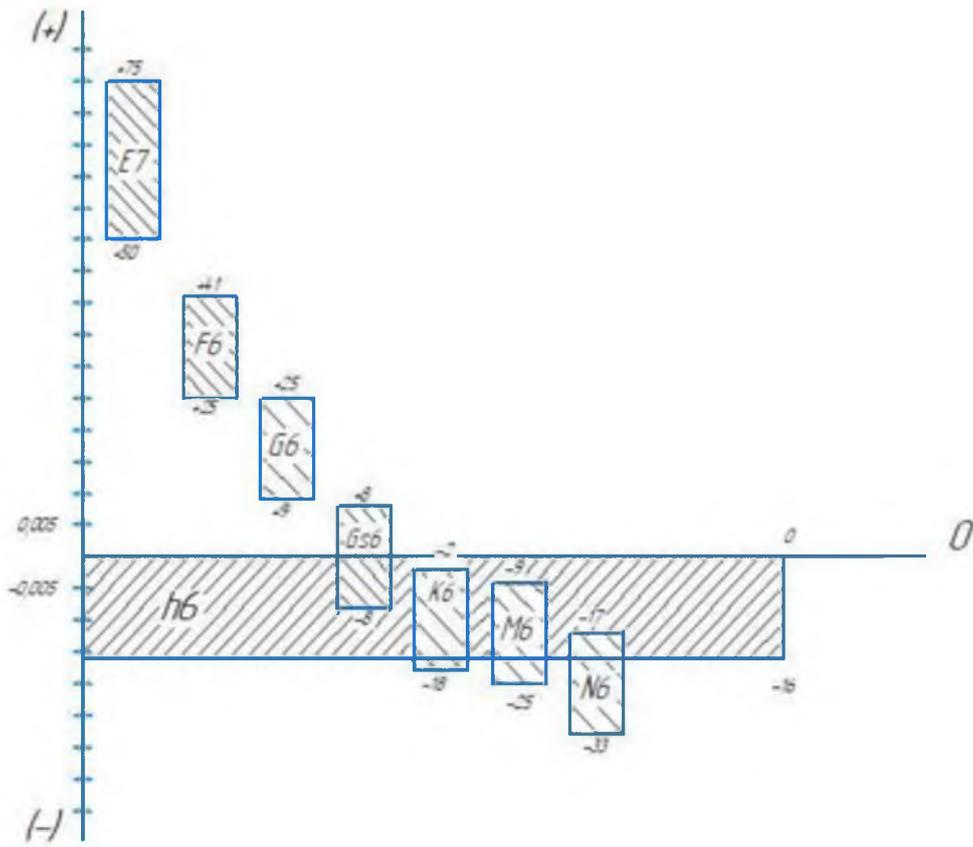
Схема расположения полей допусков в системе вала
